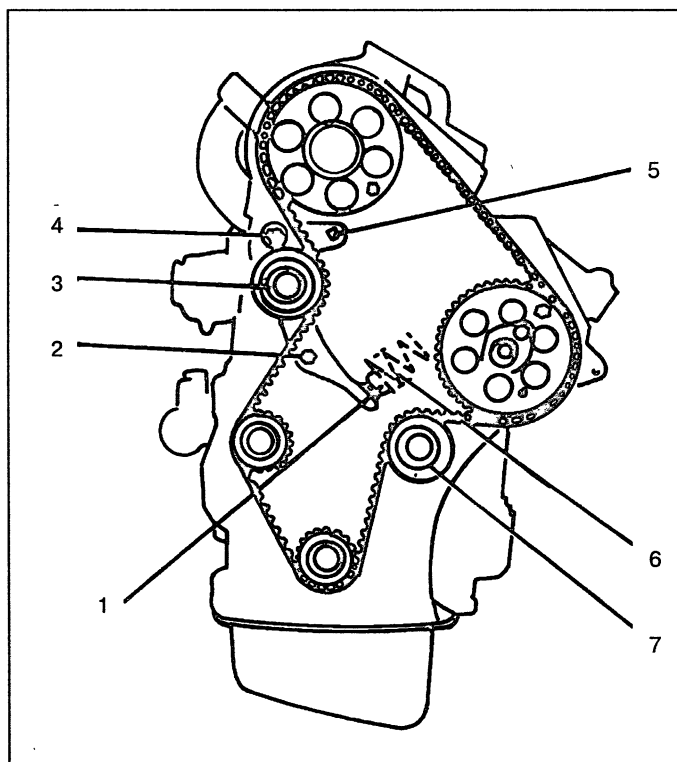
Снятие и установка ремня газораспределительного механизма: 1 – плунжер; 2 – гайка; 3 – ролик натяжителя; 4 – болт; 5 – отверстие квадратной формы; 6 – пружина; 7 – неподвижный ролик
